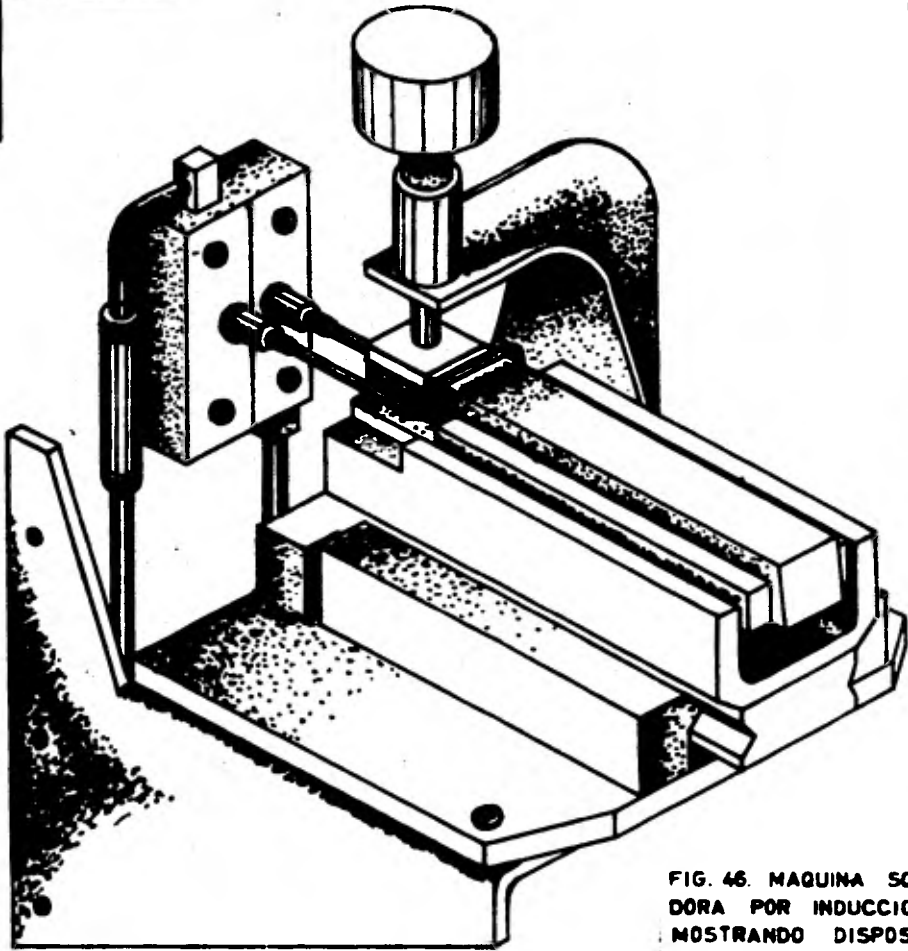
MAQUINA SOLDADORA POR INDUCCION MOSTRANDO DISPOSITIVO DE FIJACION PARA SOLDAR BURILES DE PASTILLA DE WC.
